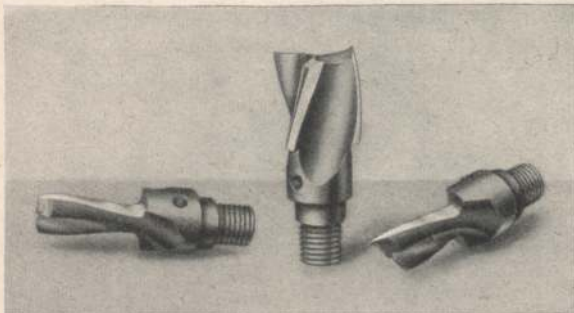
Werkzeug-Abbildungen, wie sie für die „Holz-Her“-Maschine verwendet werden. Mit den eigenartig konstruierten Fräsern können Zapfen bis zu 12 cm Länge gleichzeitig mit Zapfenfasen angefräst werden.
